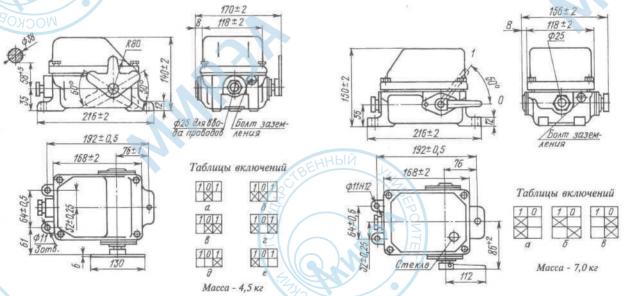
Габаритные, установочные размеры и масса выключателя типа КУ-744
